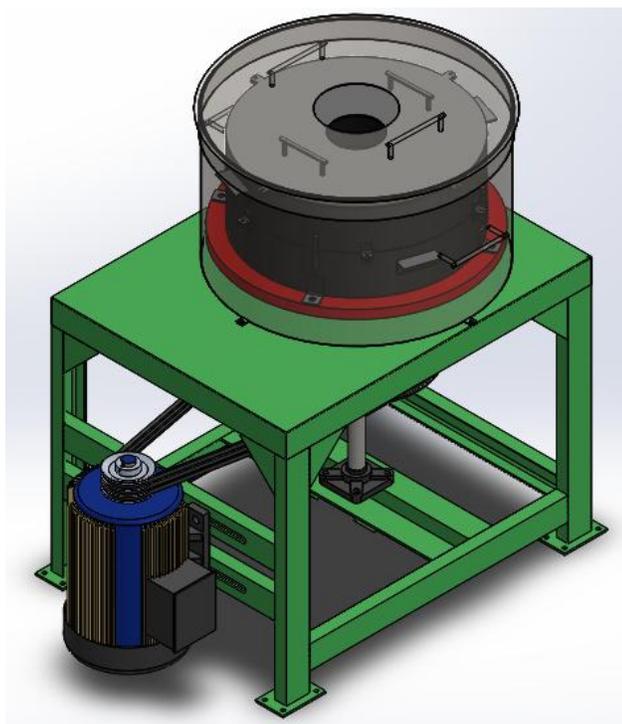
Arquitectura propuesta para la máquina de fundición centrifuga vertical
